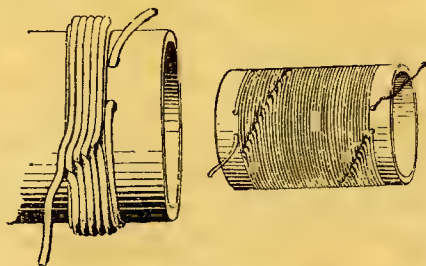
Способ намотки и общий вид готовой двуслойной катушки.
